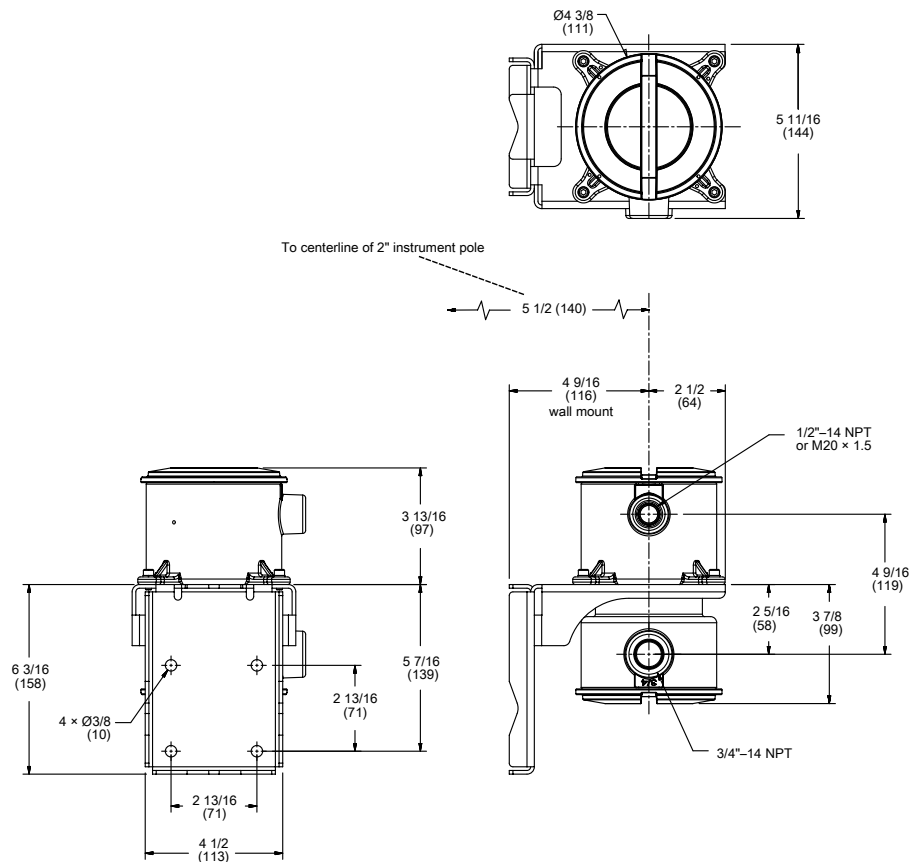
Dimensions de la platine processeur avancée déportée
